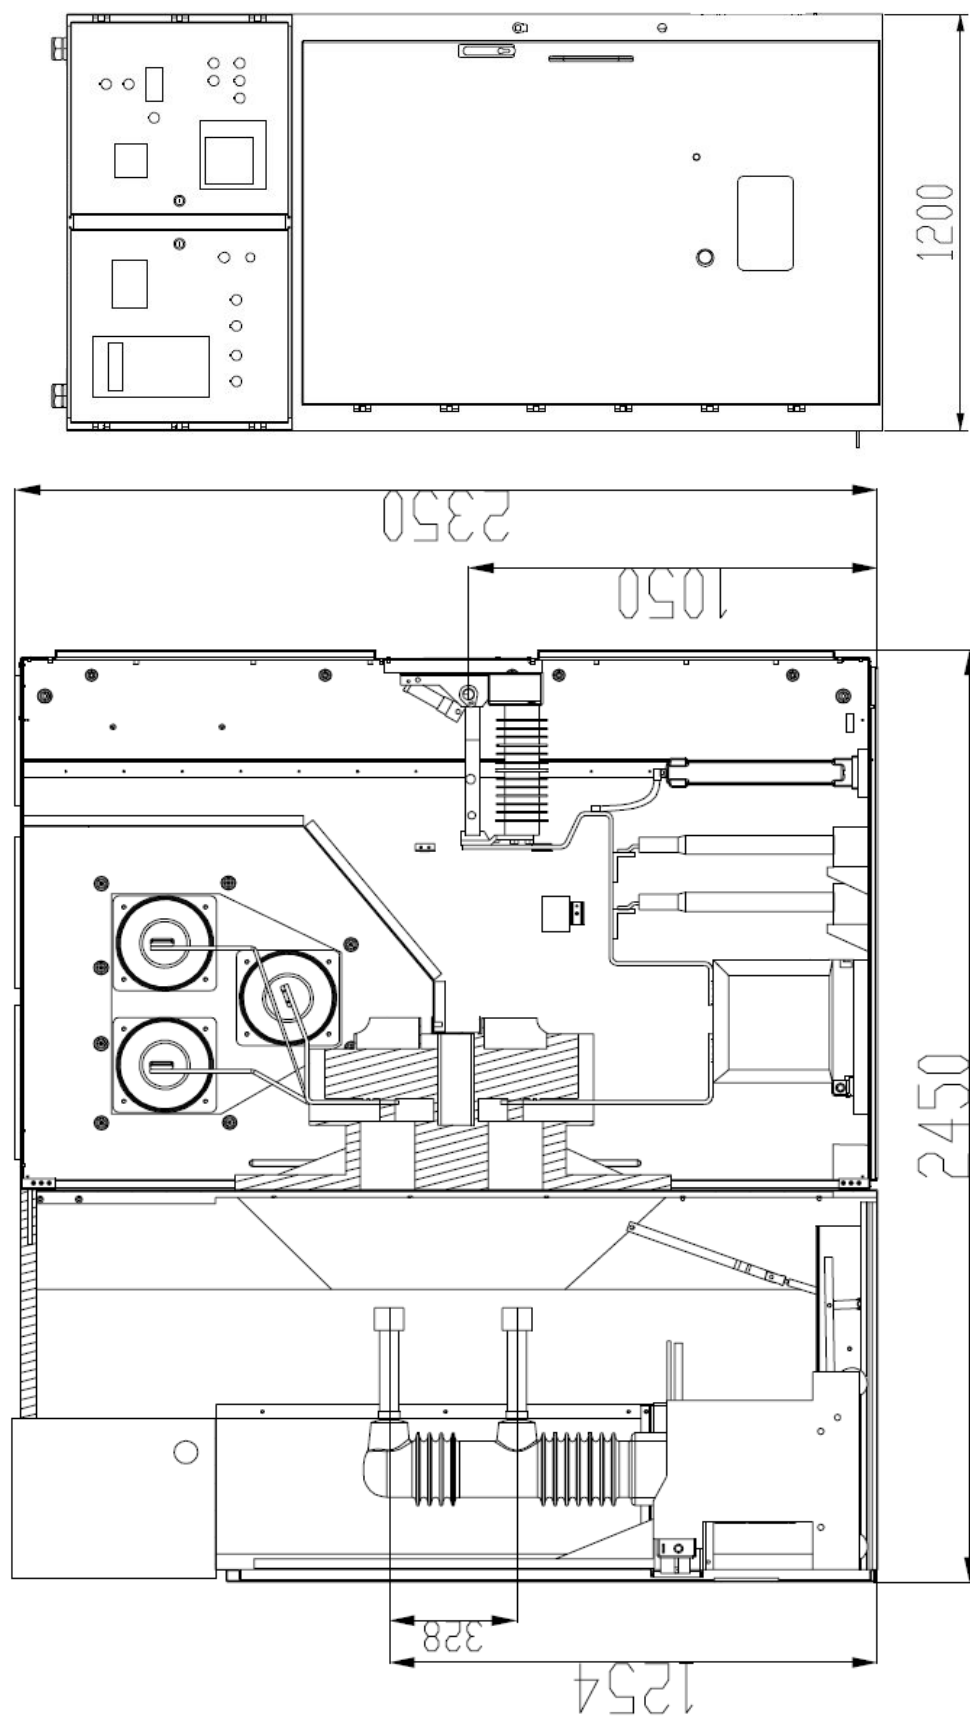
Размеры КРУ-35 КВ, разрез, шинный ввод сверху
